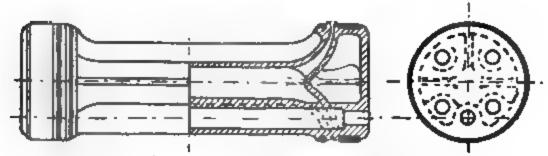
1122. Kolbenschieber einer Walzenzugmaschine. D=750, H=1100, n=50, p=5.5 Atm. (Zeitechr. d. V. d. Ing. 1891). 1:2.
